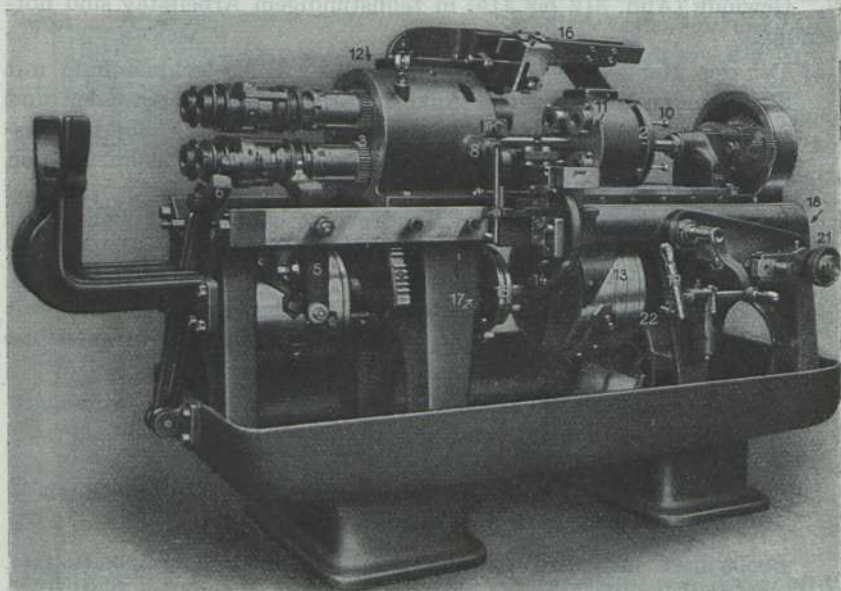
Vierspindelautomat von Gildemeister & Co., A. G., Bielefeld.
